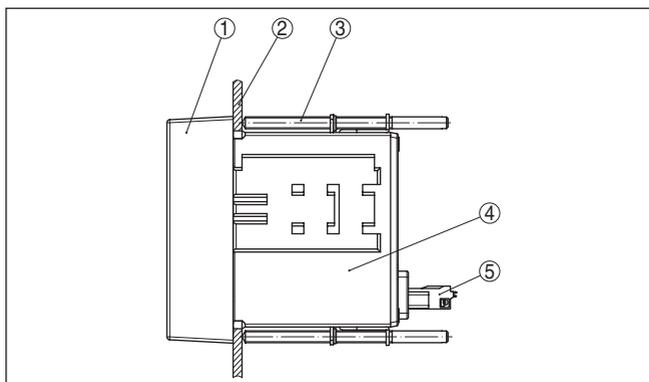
VEGADIS 82 per montaggio a fronte-quadro
